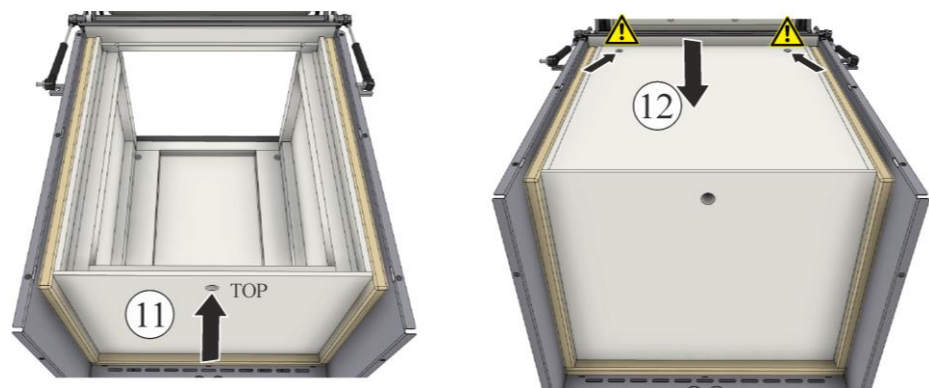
Montaje del aislamiento de la pared posterior y del techo (figura análoga)
